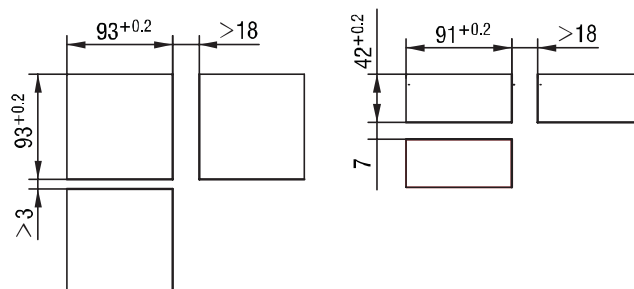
Montaje en panel para TRM210-H1 (izquierda) y TRM210-H2 (derecha)
